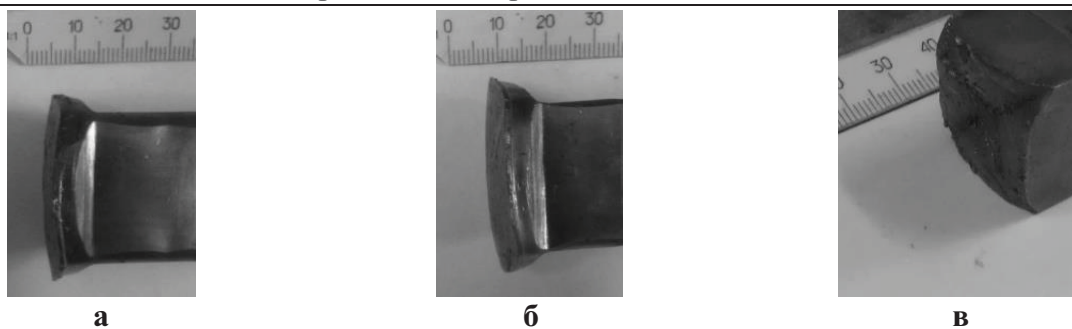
Протяжка короткой заготовки с промежуточным профилированием на катушку
